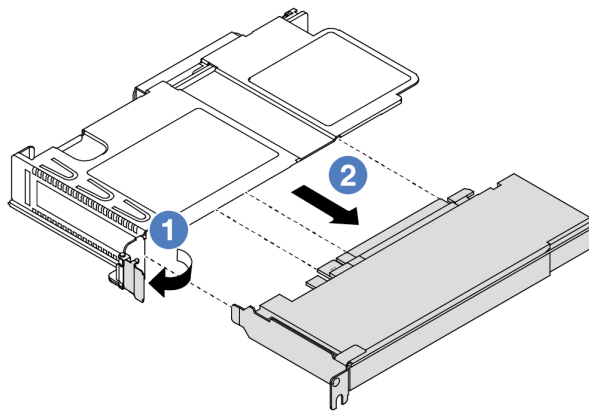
Remoção do adaptador PCIe do conjunto de placa riser LP-FH frontal
